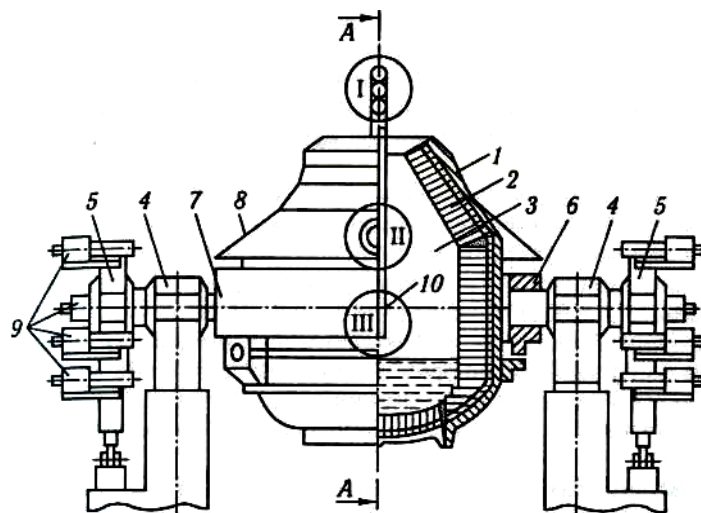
Кисневий конвертор: – корпус; 2 – футерівка; 3 – внутрішня порожнина; 4 – опорні вузли на станинах; 5 – корпус веденого зубчастого колеса; 6 – цапфа; 7 – опорне кільце з цапфами і системами кріплення в ньому корпусу; 8 – захисний кожух; 9 – електродвигуни навісного типу з редукторами; 10 – киснева фурма.
